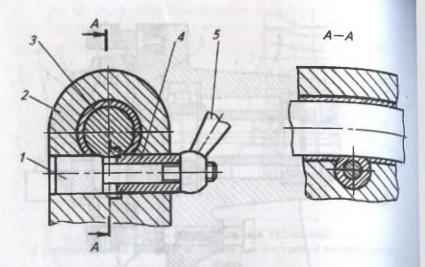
Прижимное устройство: 1 - головка винта; 2 -корпус; 3 - вал поворотной части; 4 - сухарь; 5 - рукоятка
